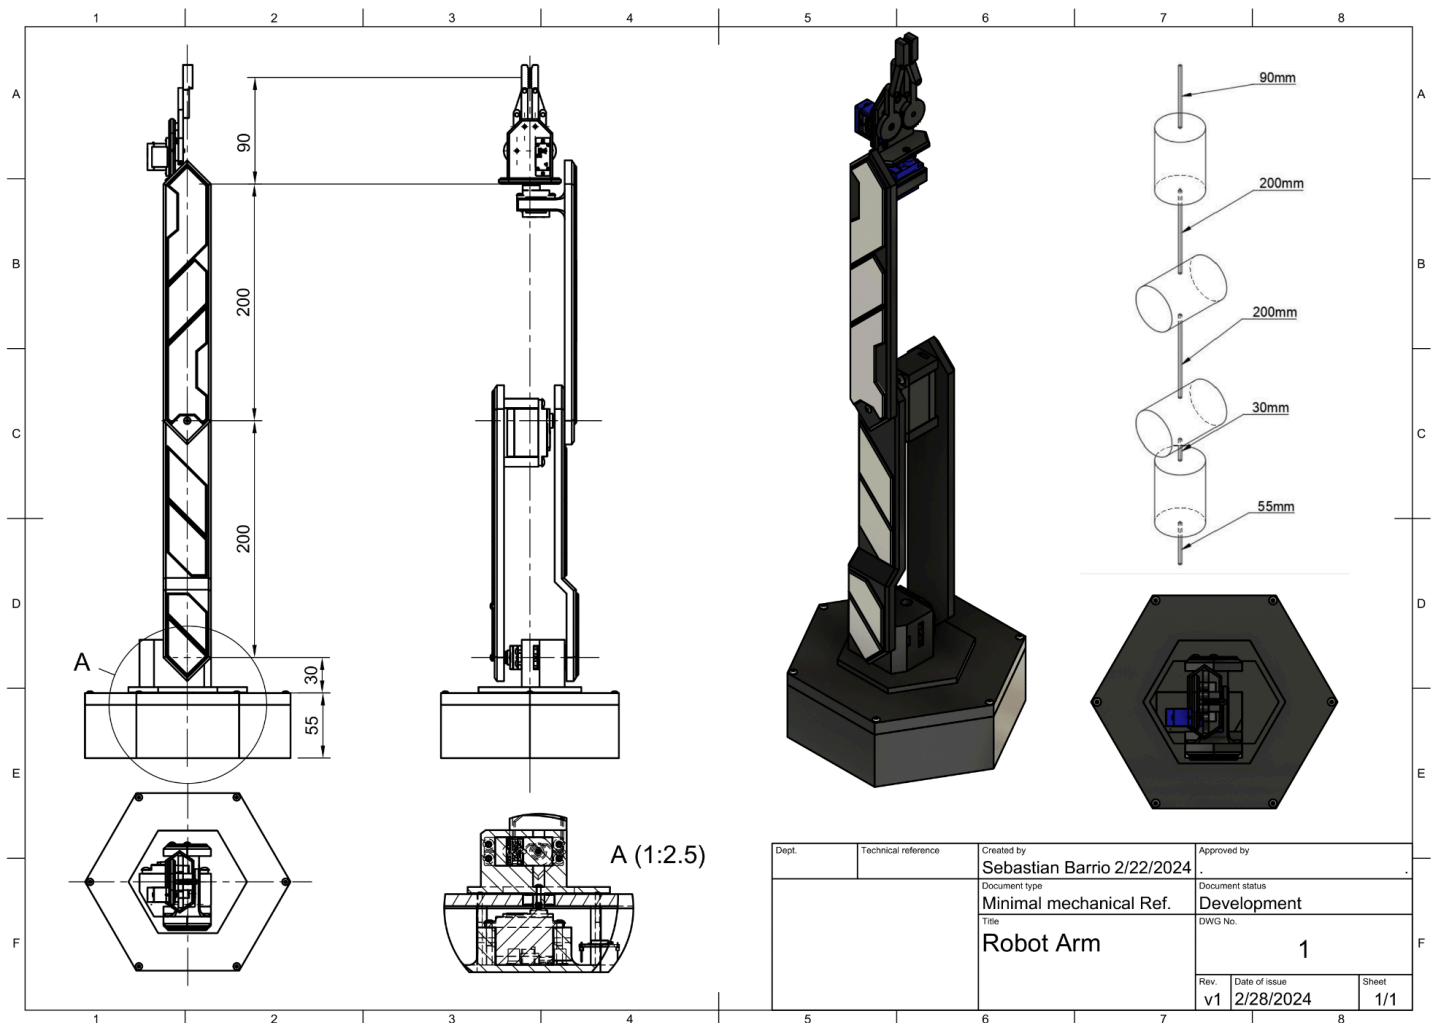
Dibujo técnico del cad, vista frontal, lateral, superior e isométrica, sección interna del servo de la base (A) y configuración cinemática ([link al cad](#))
